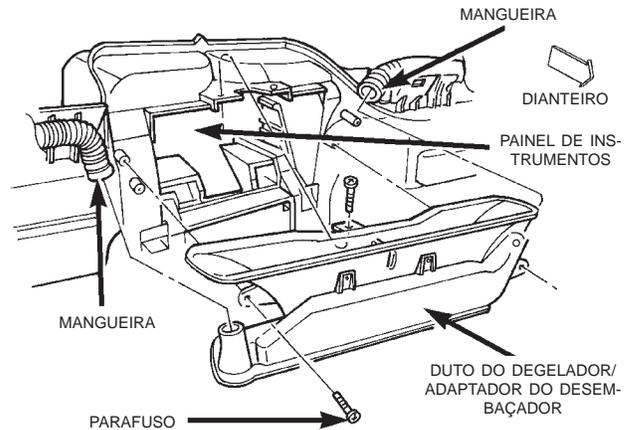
Duto do Degelador/Adaptador do Desembaçador
